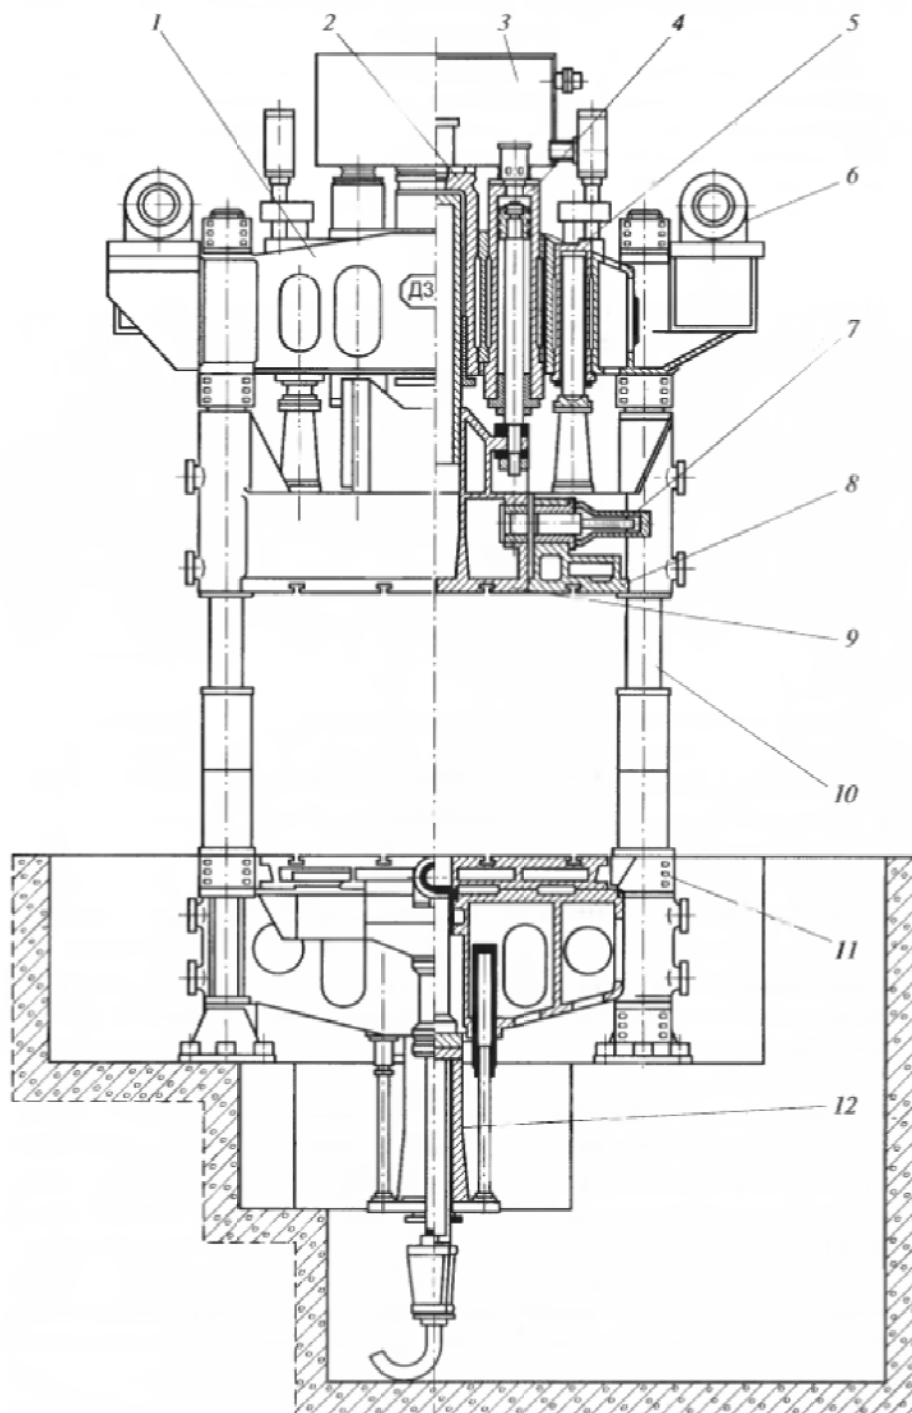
Конструкция гидравлического листоштамповочного пресса двойного действия:
